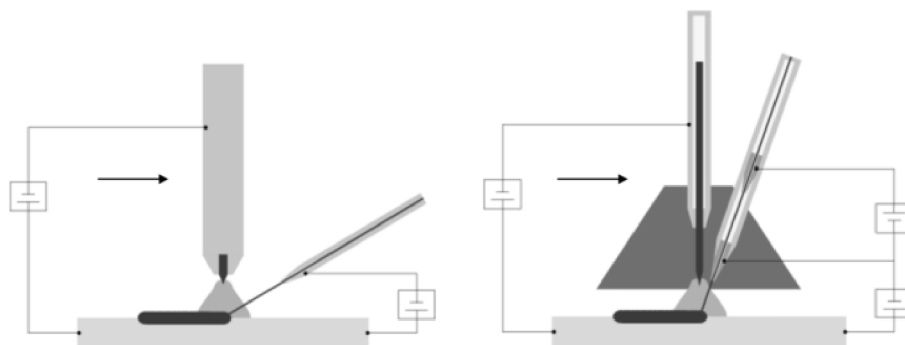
Automatizovaný proces TIG [32]. Obr. 21 Detail hořáku s podavačem [32].
